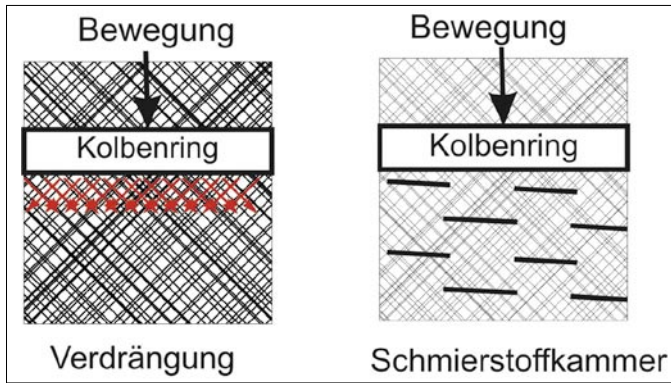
Verdrängung der Schmiermittel in den Honnillen und die Schmiertaschen der Laserbearbeitung
